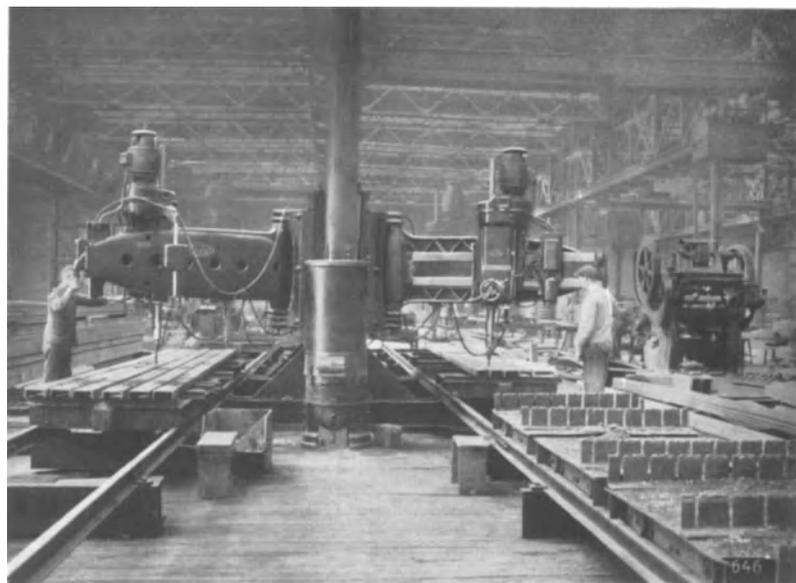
Bohrvorlagen in einer Eisenkonstruktionswerkstätte
